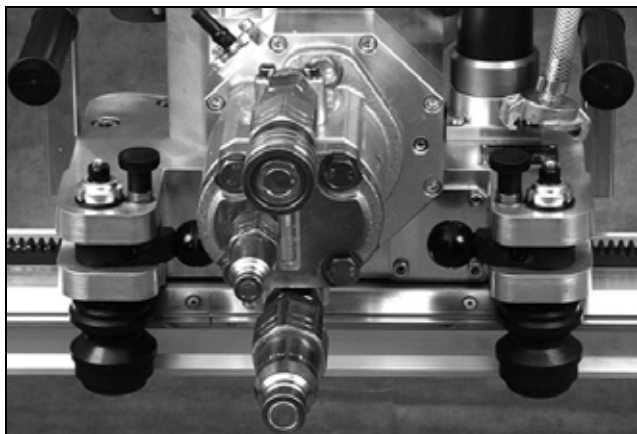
Гидравлический приводной двигатель отрезного диска смонтирован
